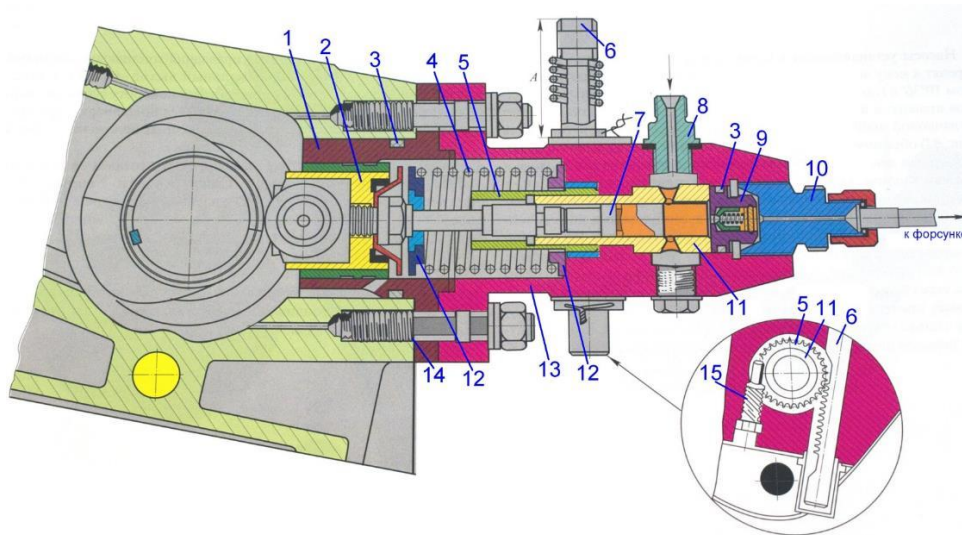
Эскиз топливного насоса 5Д49: 1 - направляющая втулка толкателя; 2 - толкатель; 3 - резиновые кольца; 4 - пружина; 5 - поворотная шестерня; 6 - рейка; 7 - плунжер; 8, 10 - штуцера; 9 - корпус нагнетательного клапана; 11 - гильза плунжера; 12 - тарелки плунжера; 13 - корпус насоса; 14 - регулировочные прокладки; 15 - регулировочный винт.
